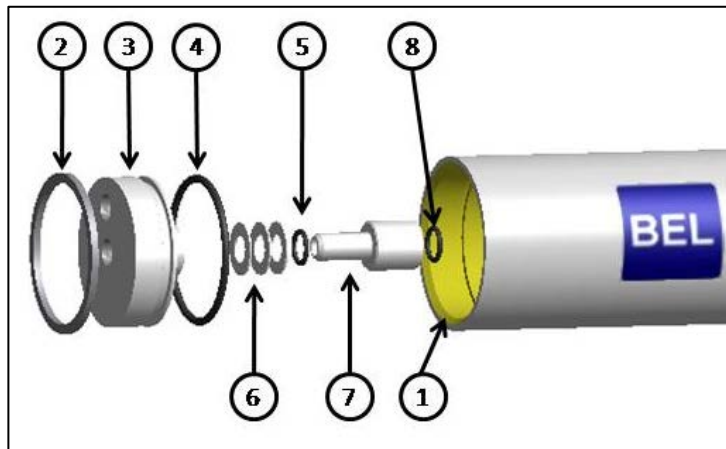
Despiece Cabeza tubo BEL 4" 300/450 psi – Endport
